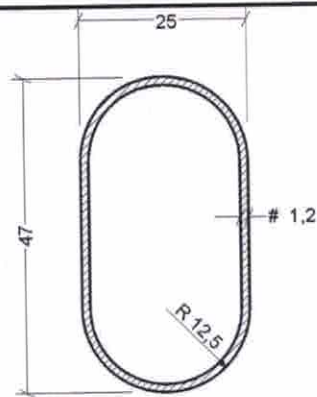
Corte DD' – Tubo de perfil oblongo (medidas em milímetros)
